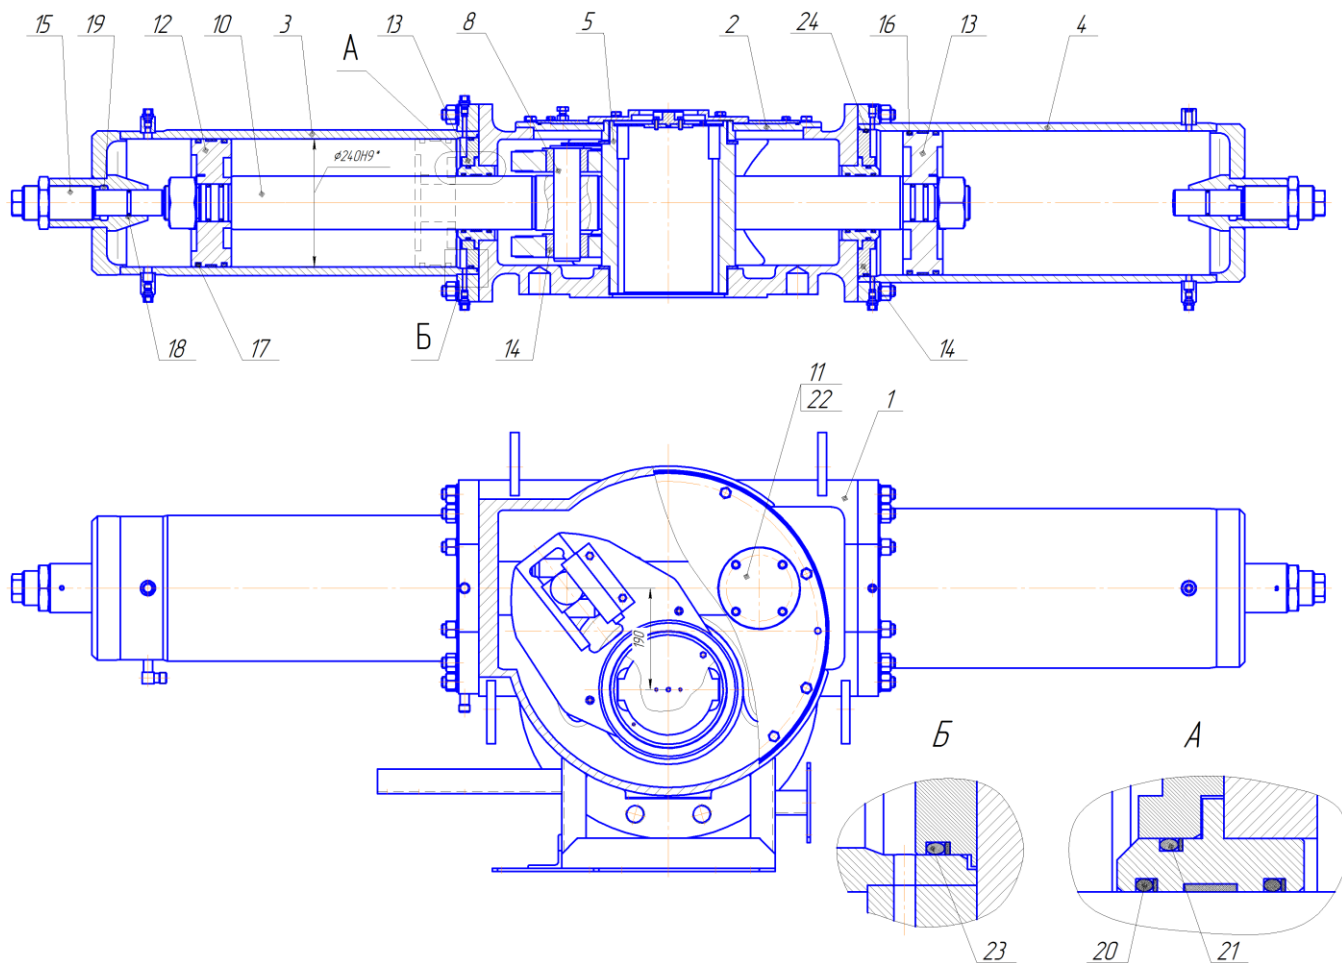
а – Пневмогидропривод с резервными ресиверами
